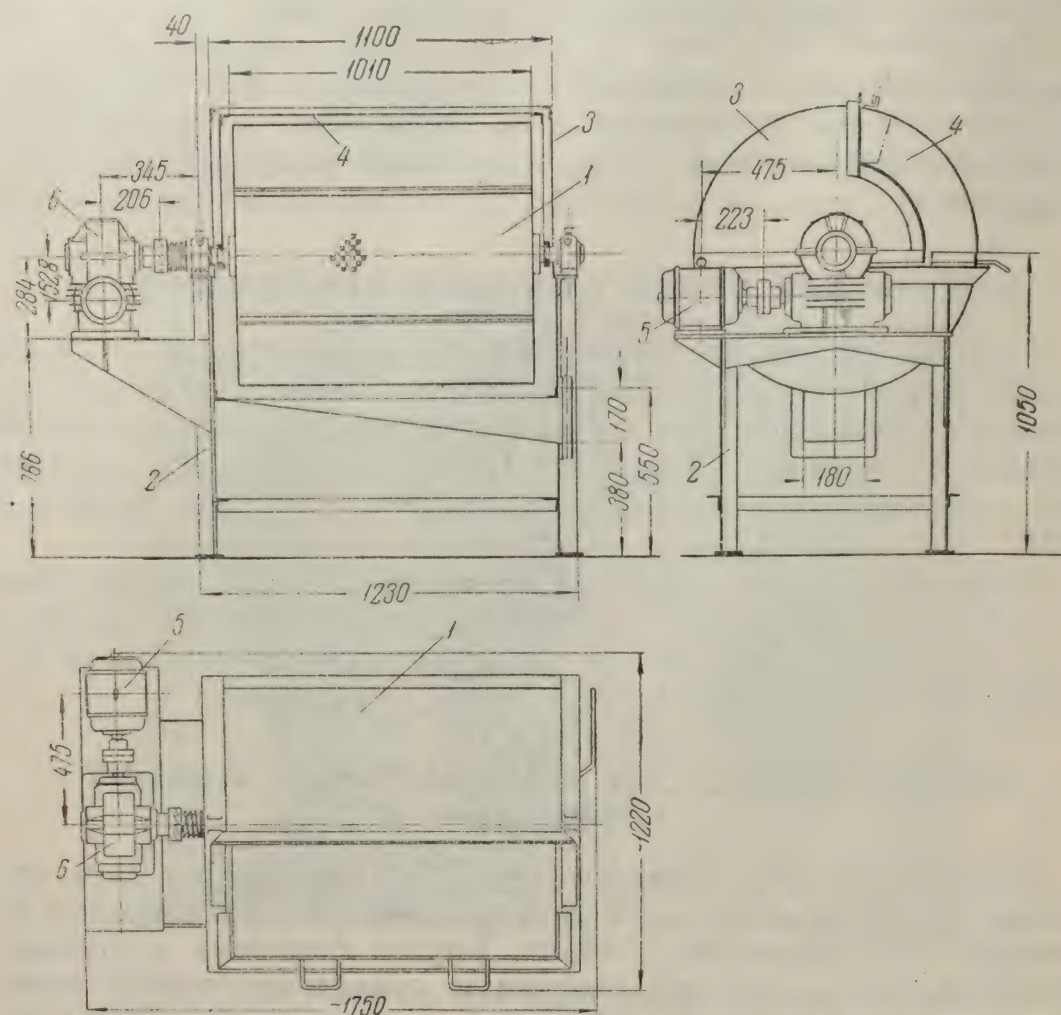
Барабан типа БСН для промывки, очистки и шпарки субпродуктов:
